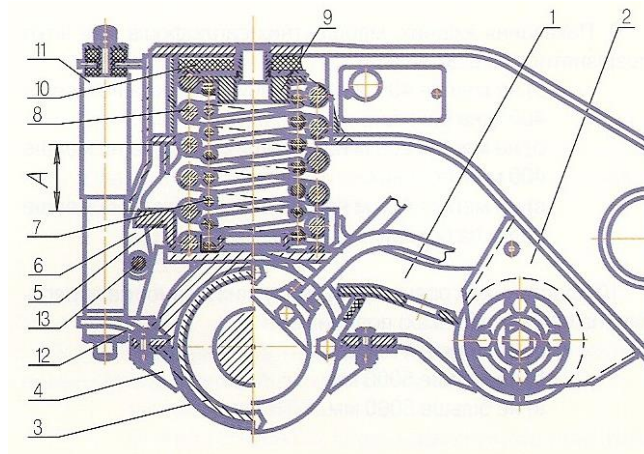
З'єднання колісної пари з рамою і буксовими ресорне підвищення: 1 - важіль; 2, 6 - кронштейн рами візка; 3 - корпус букси; 4 - хомут; 5 - кронштейн; 7,8 - циліндрична гвинтова пружини; 9 - центровиків; 10 - гумовий амортизатор; 11 - гідравлічний гаситель коливань; 12 - кронштейн буксового вертикального гасителя; 13 - вісь
